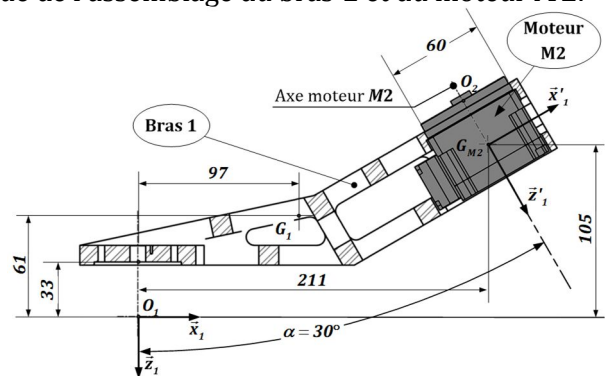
Dessin de l'assemblage du bras 1 et du moteur M2
